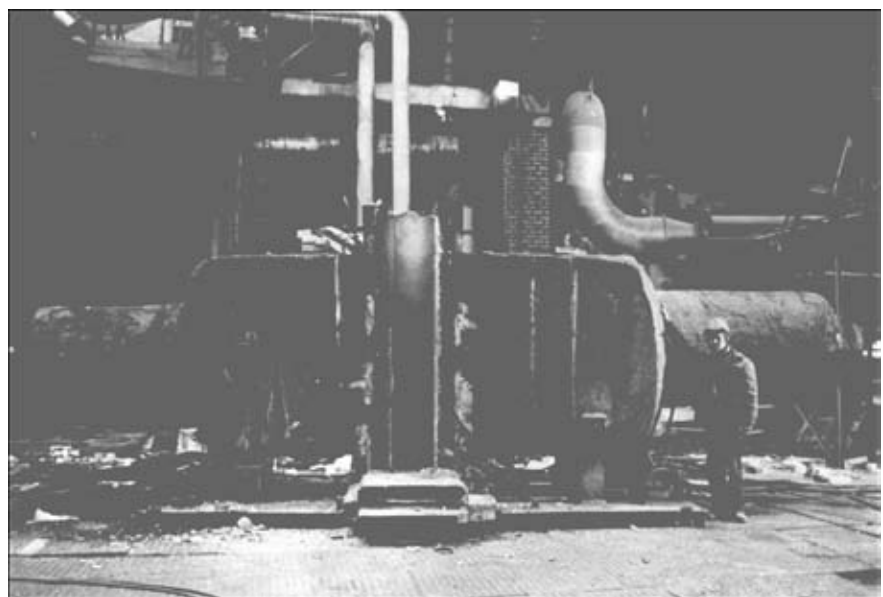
Укрупненная способом ЭШС КПКМ кованосварная заготовка рабочего вала из стали 50ХН массой 103 т для стана ЛП04500
